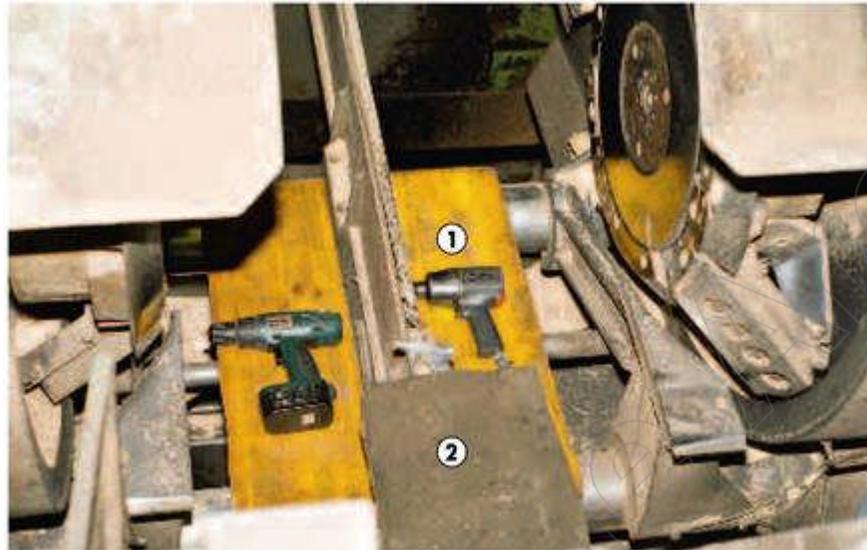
Fehlende Standfläche zum Werkzeugwechsel an einem Spaner
